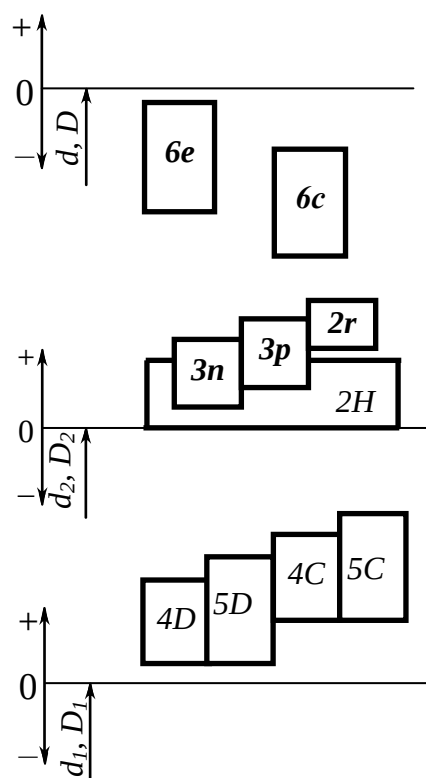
Схема полей допусков резьбовых соединений с натягом
